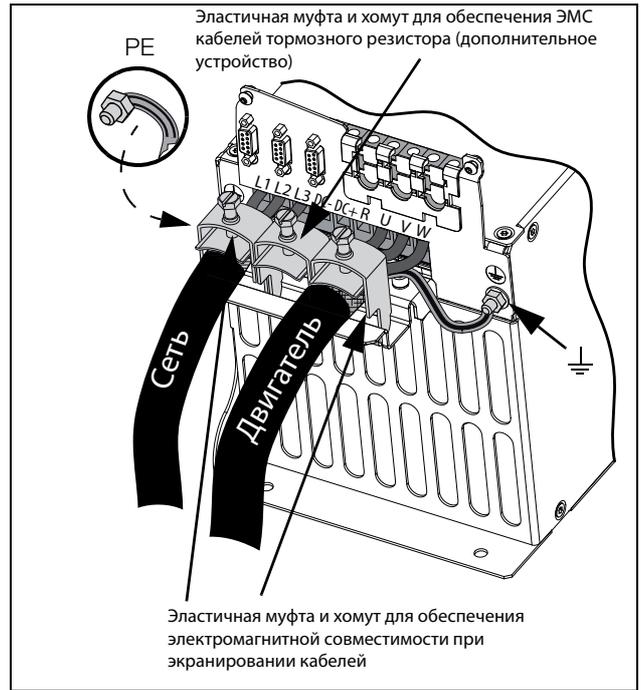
Подключение сетевого питания и двигателя моделей 48-025 — 48-058, размер корпуса С2 и моделей 69-002 — 69-025, размер корпуса С2(69)
